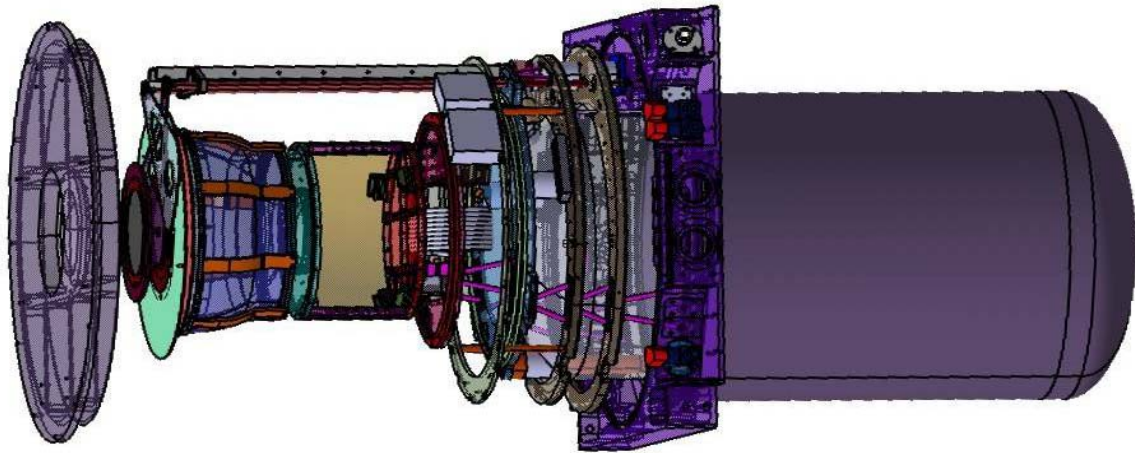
Vue d'ensemble en 3D de la caméra bolométrique dessinée sur CATIA.
